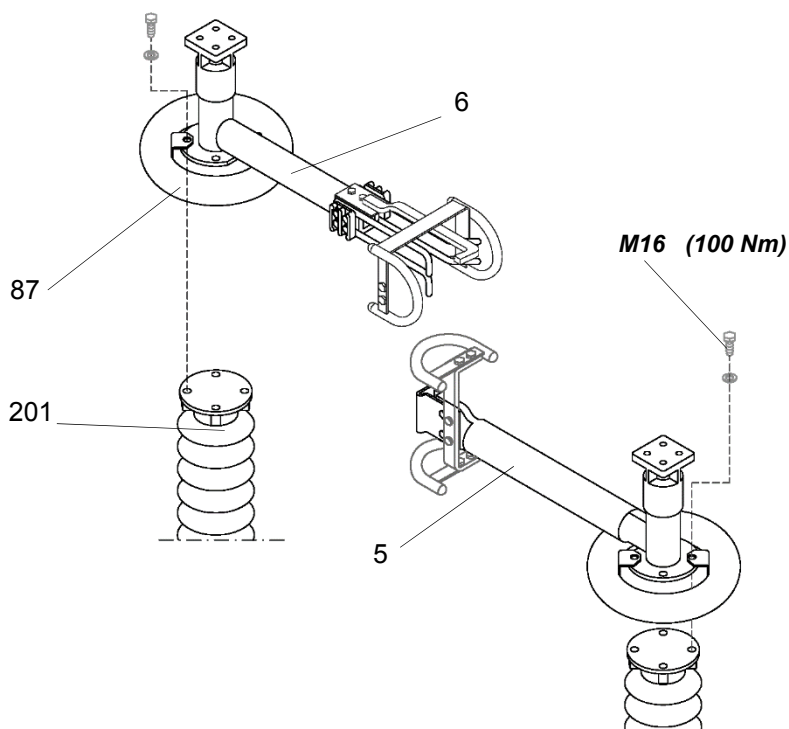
Montaż odłącznika: Instalacja bieguna całkowicie zmontowanego na konstrukcji wsporczej
